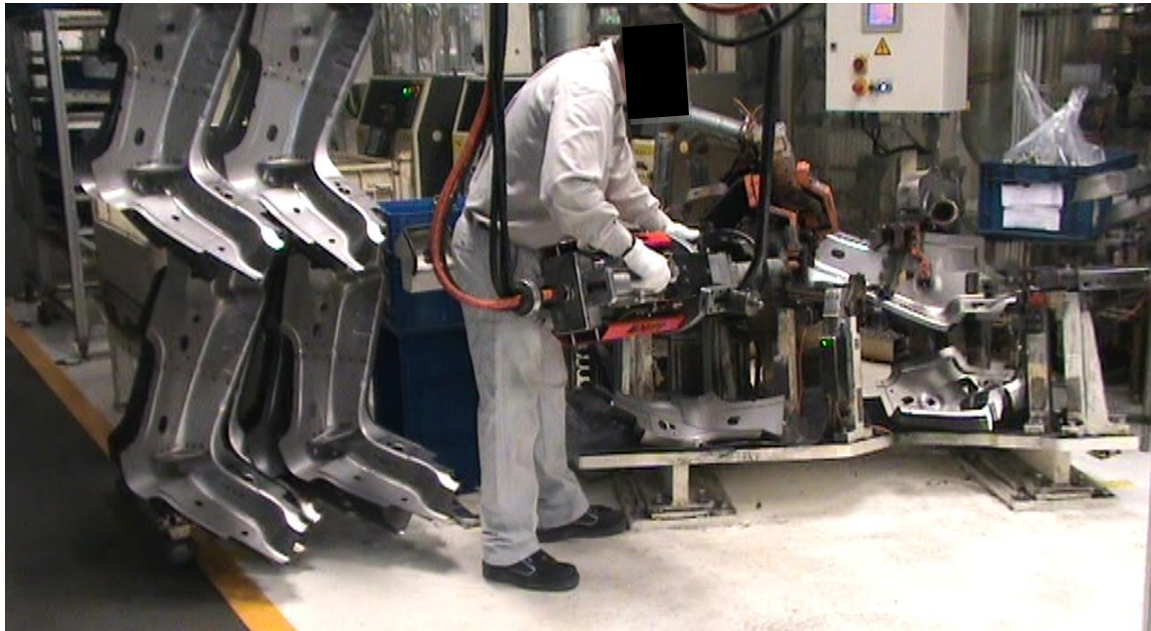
Situação K : Manipulação da pistola de soldadura
